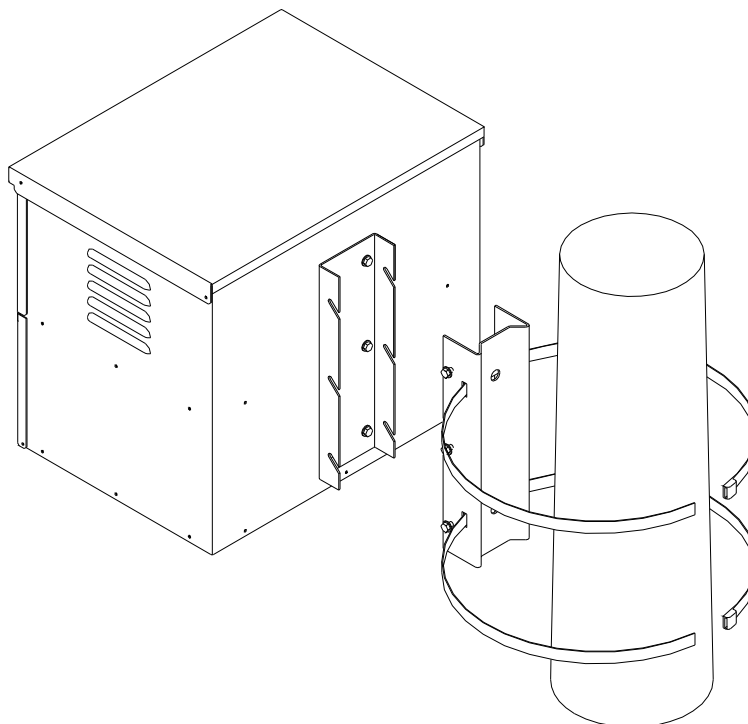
Instalação do Gabinete Externo utilizando abraçadeiras metálicas.
